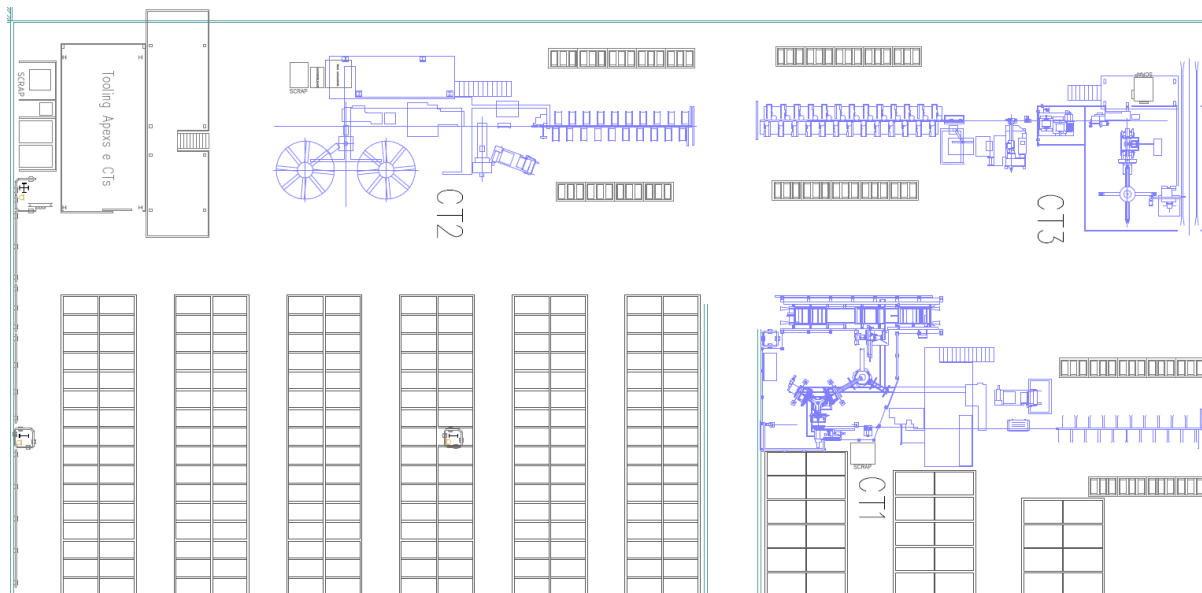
Layout alternativo para área de construção de núcleos de talão
